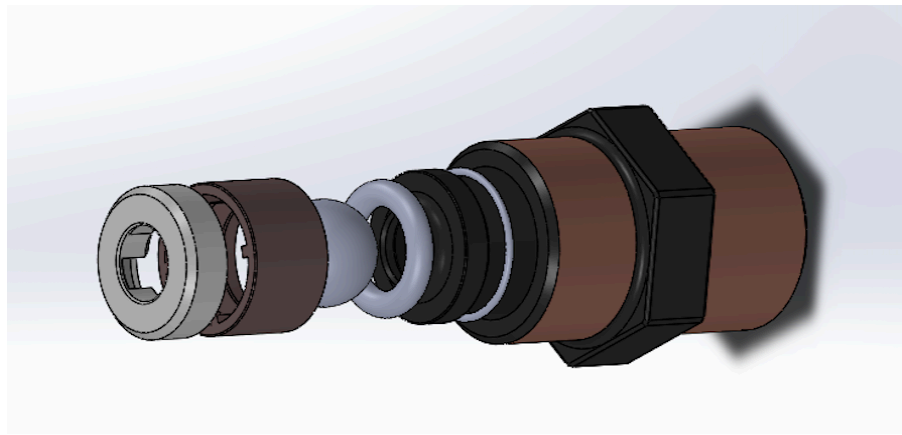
Explosionado del ensamblaje (Fuente propia)
